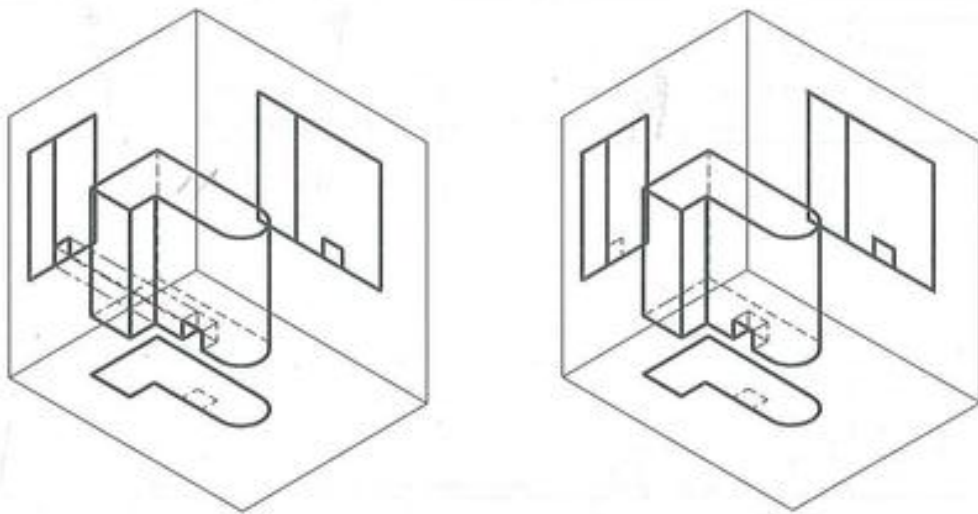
Resultado de las proyecciones sobre tres planos del paralelepípedo.
